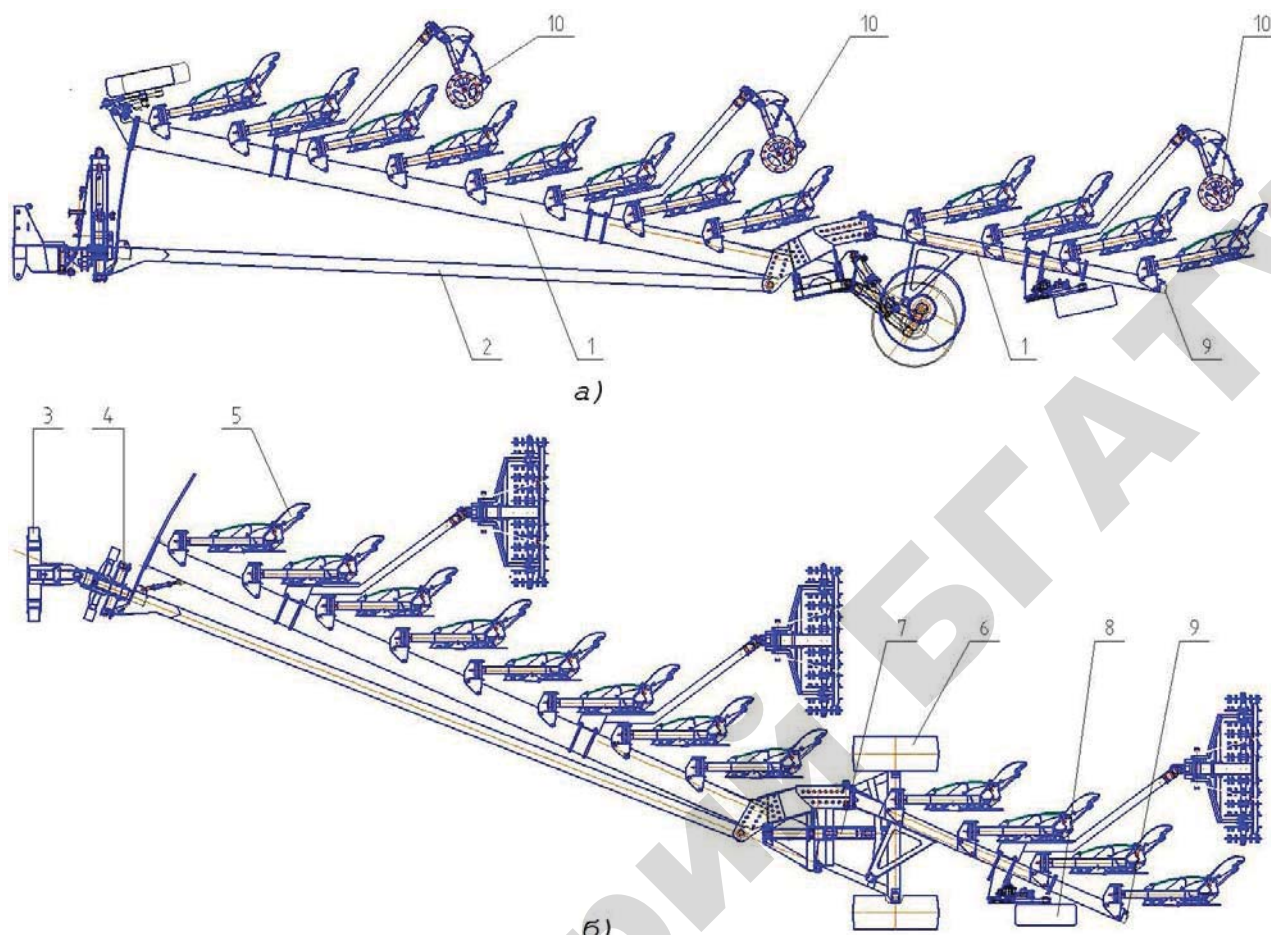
Плуг 12-ти корпусный оборотный ПО-(8+4)-40 в транспортном (а) и рабочем (б) положении: 1 – рама; 2 – тяговая балка; 3 – навеска; 4 – механизм оборота; 5 – корпус; 6 – колесный ход; 7 – гидросистема; 8 – опорное колесо; 9 – электрооборудование; 10 – приставки для дополнительной обработки почвы.
